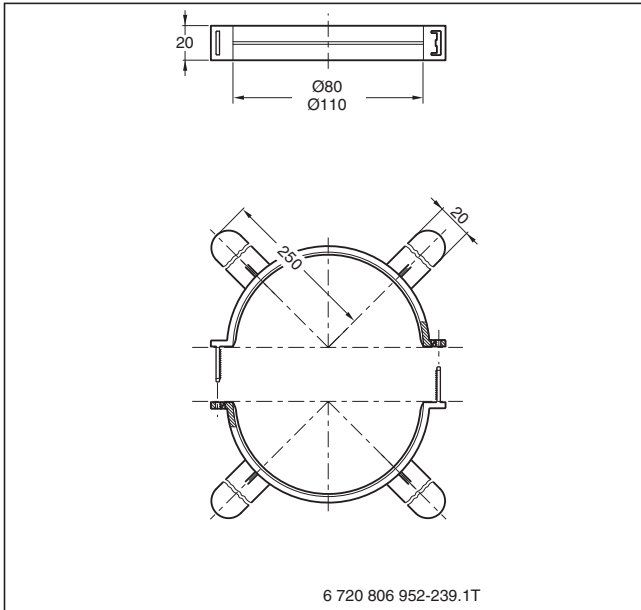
Abstandshalter für Abgasleitung im Schacht (Maße in mm)
